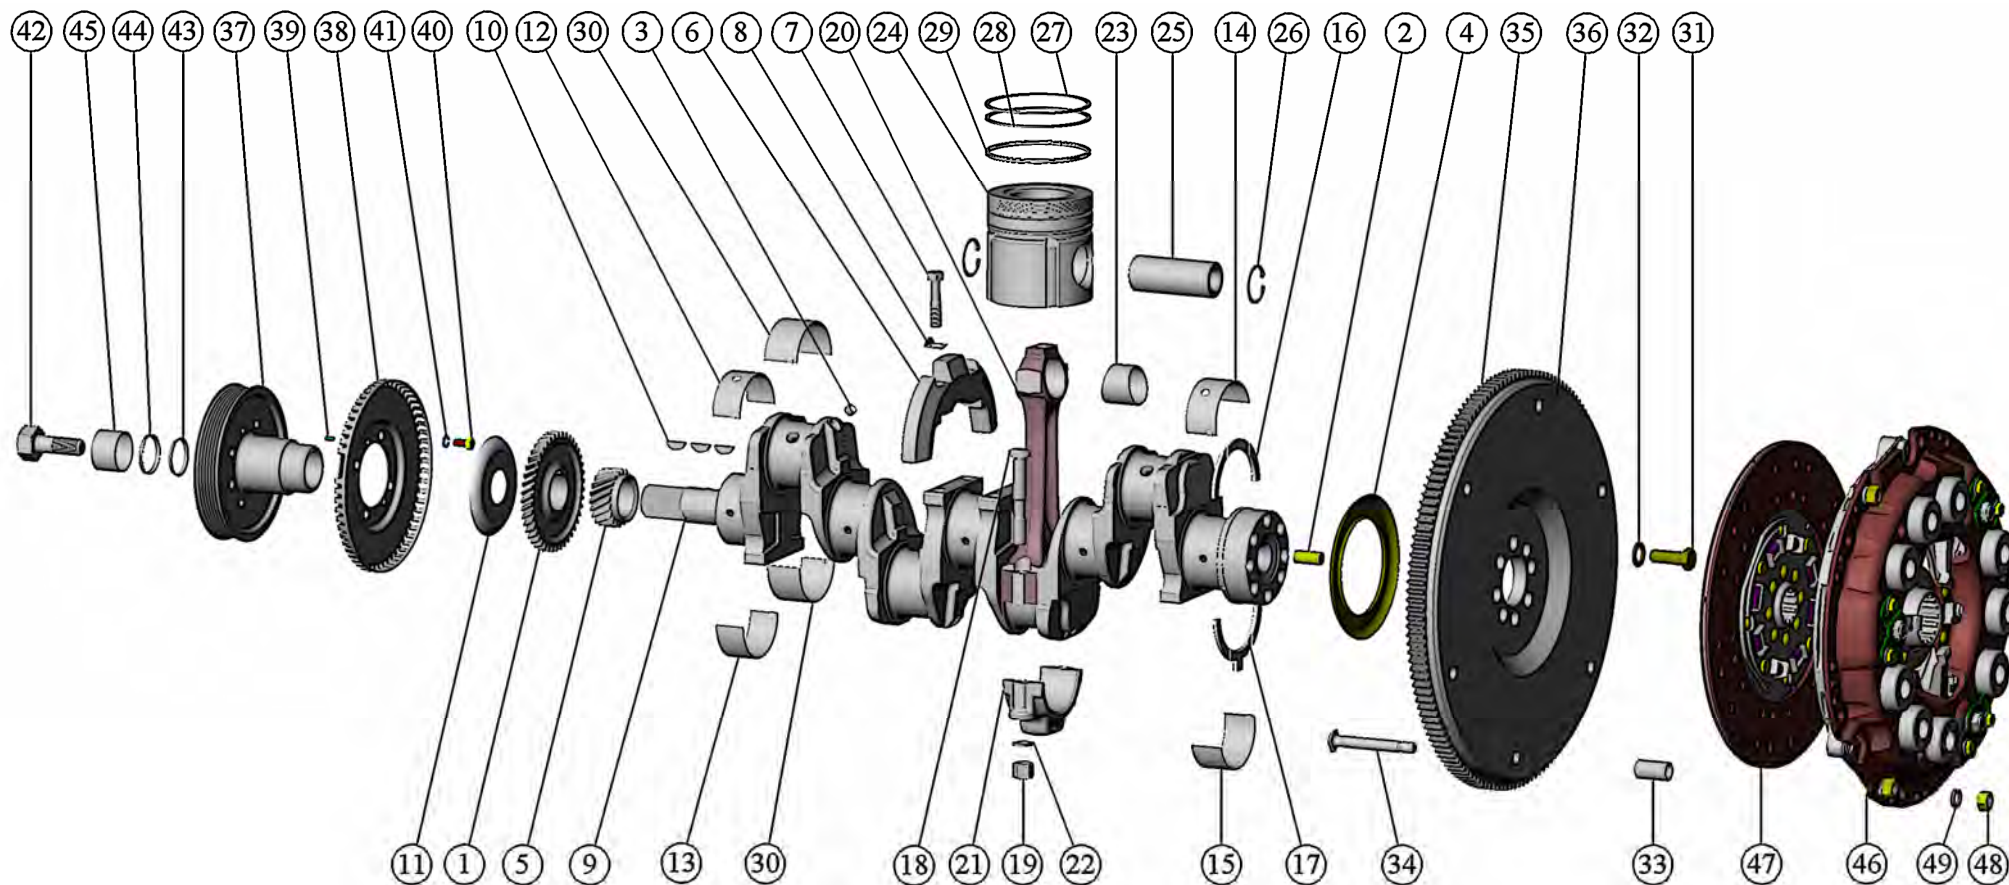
Кривошипно-шатунный механизм. Установка муфты сцепления.
